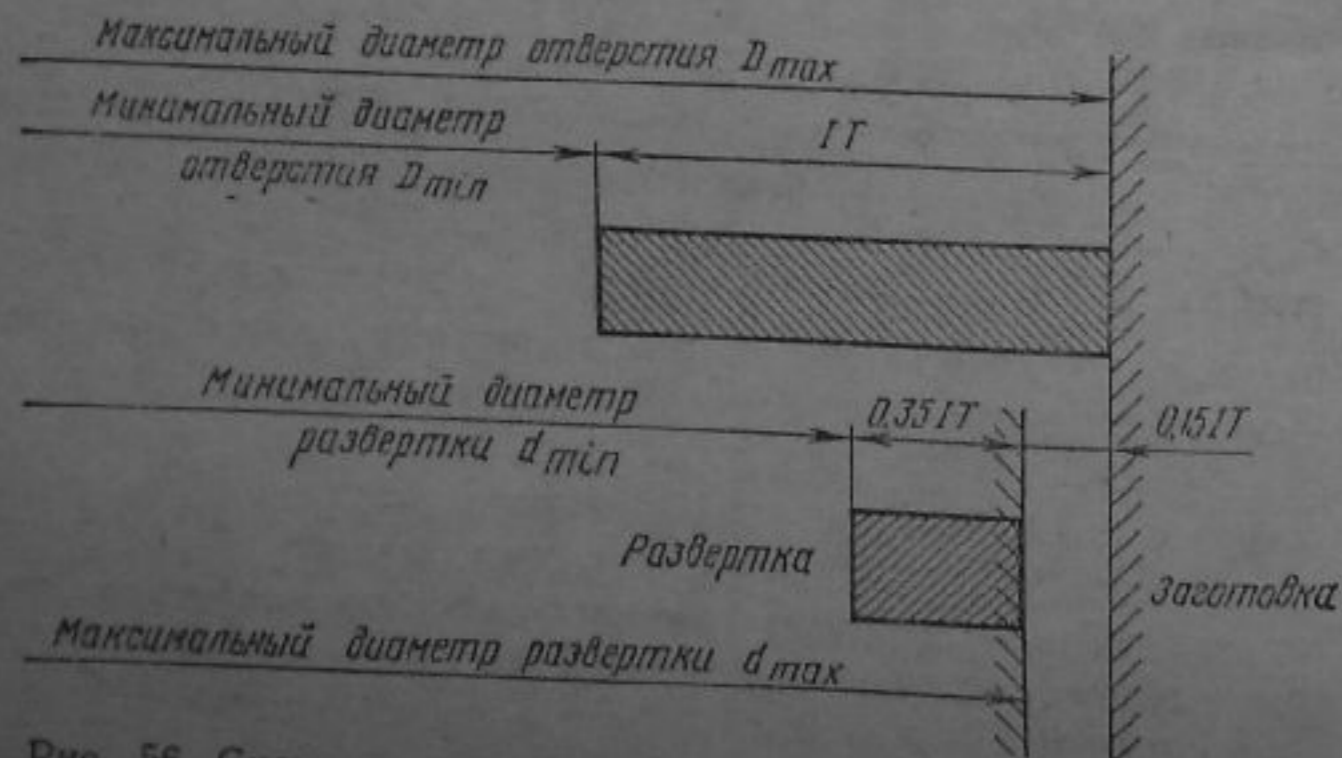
Схема расчета полей допусков и диаметров развертки
